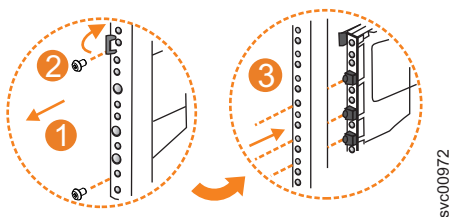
Extraiga el conjunto de rieles de la pieza de sujeción del marco frontal.
